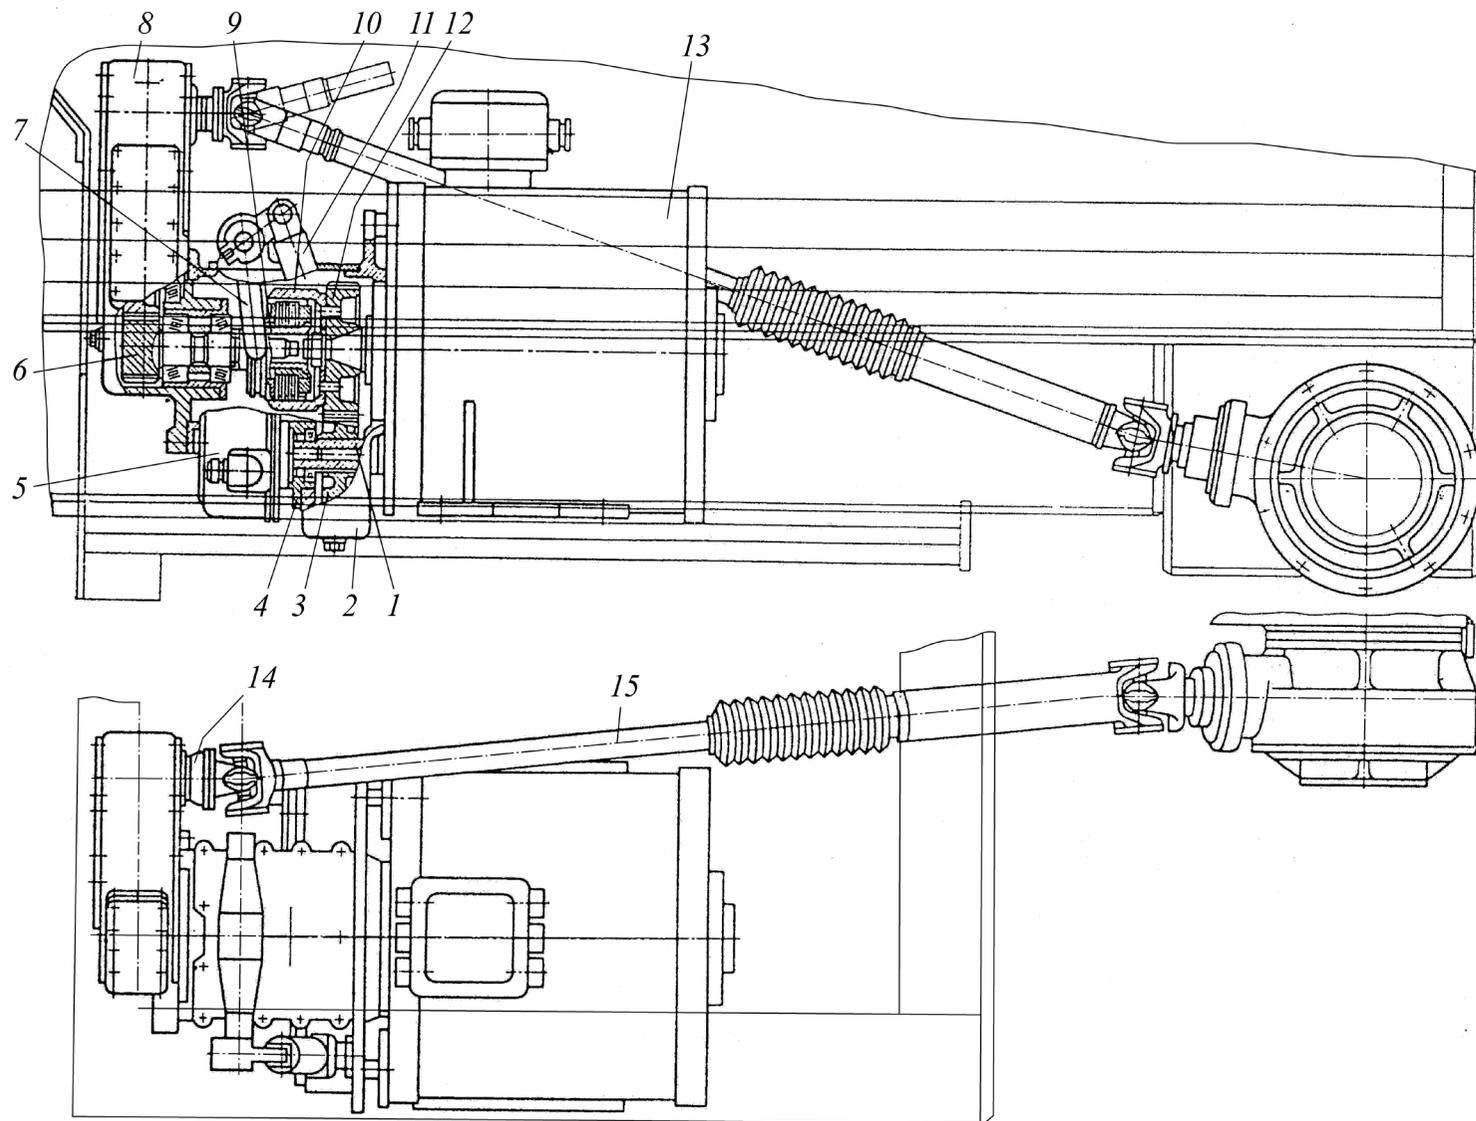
Привод конвейера: 1 – вал шестерни; 2 – редуктор маслостанции; 3 – шестерня; 4 – стакан редуктора маслостанции; 5 – насос; 6 – вал-шестерня промежуточного редуктора; 7 – вилка; 8 – редуктор промежуточный; 9 – диски ведомые; 10 – полумуфта; 11 – гидроцилиндр; 12 – шестерня ведущая; 13 – электродвигатель привода конвейера; 14 – фланец; 15 – карданный вал
